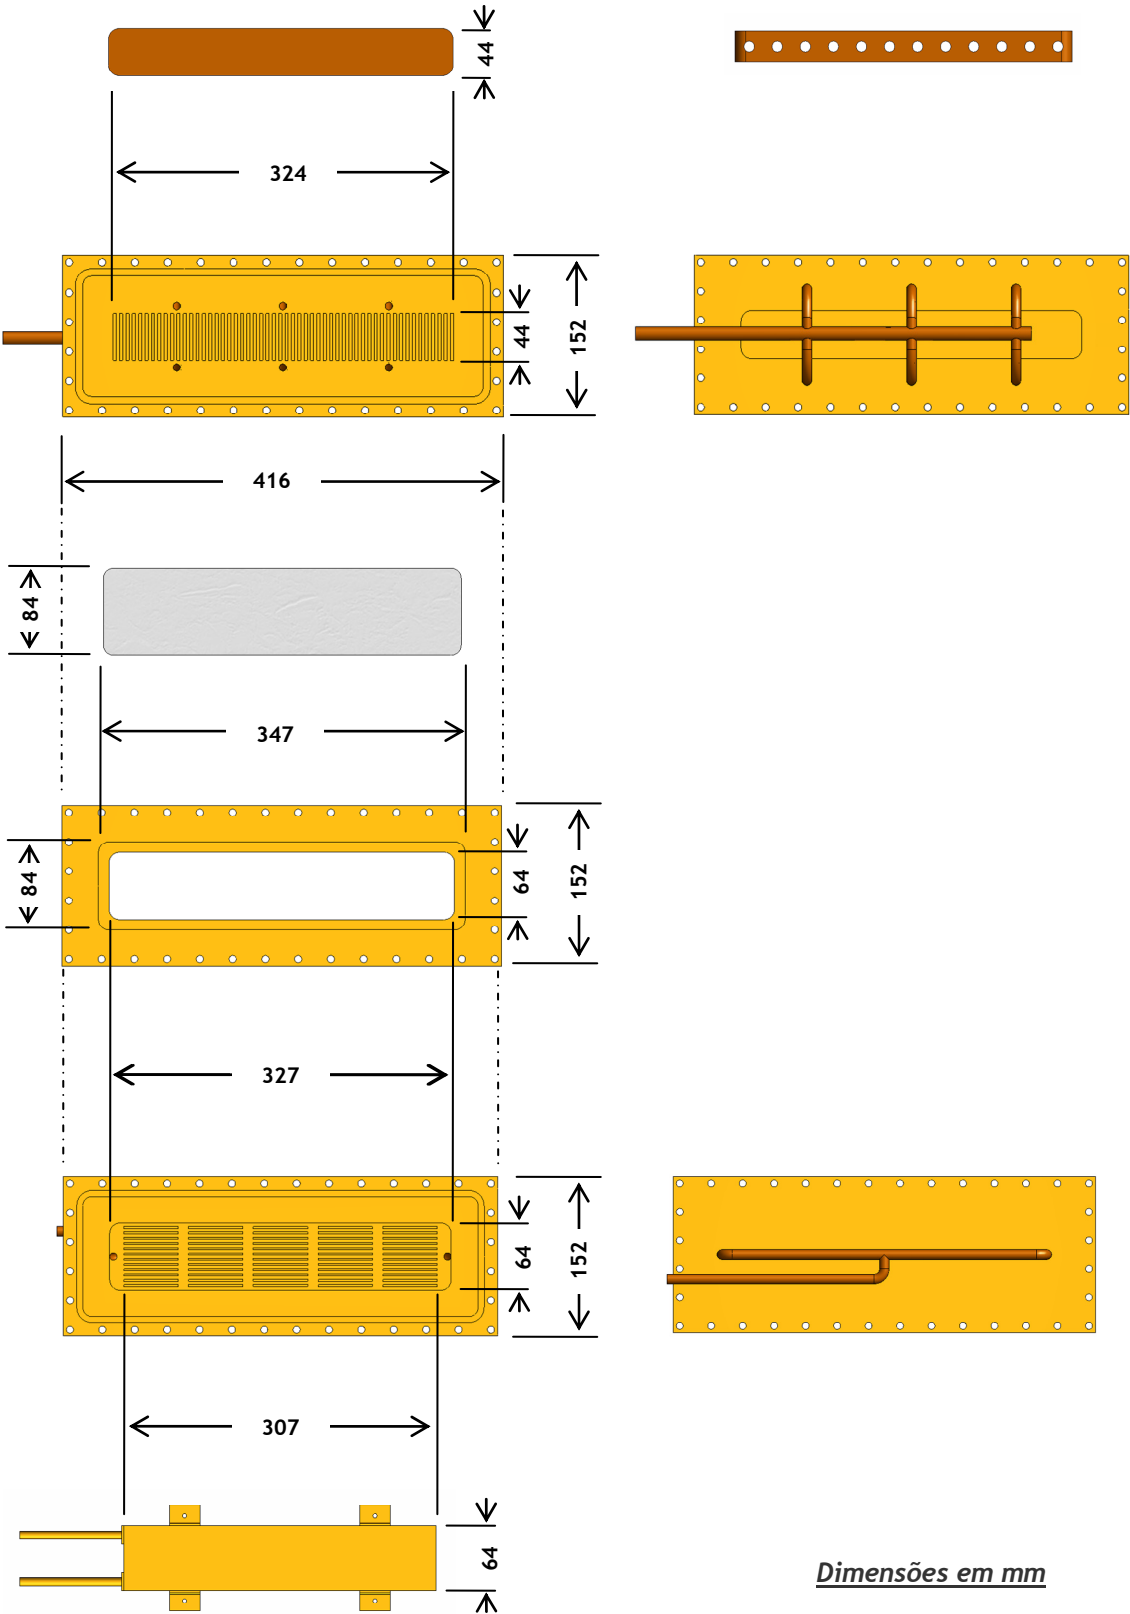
Dimensões e acoplamento das partes do evaporador
